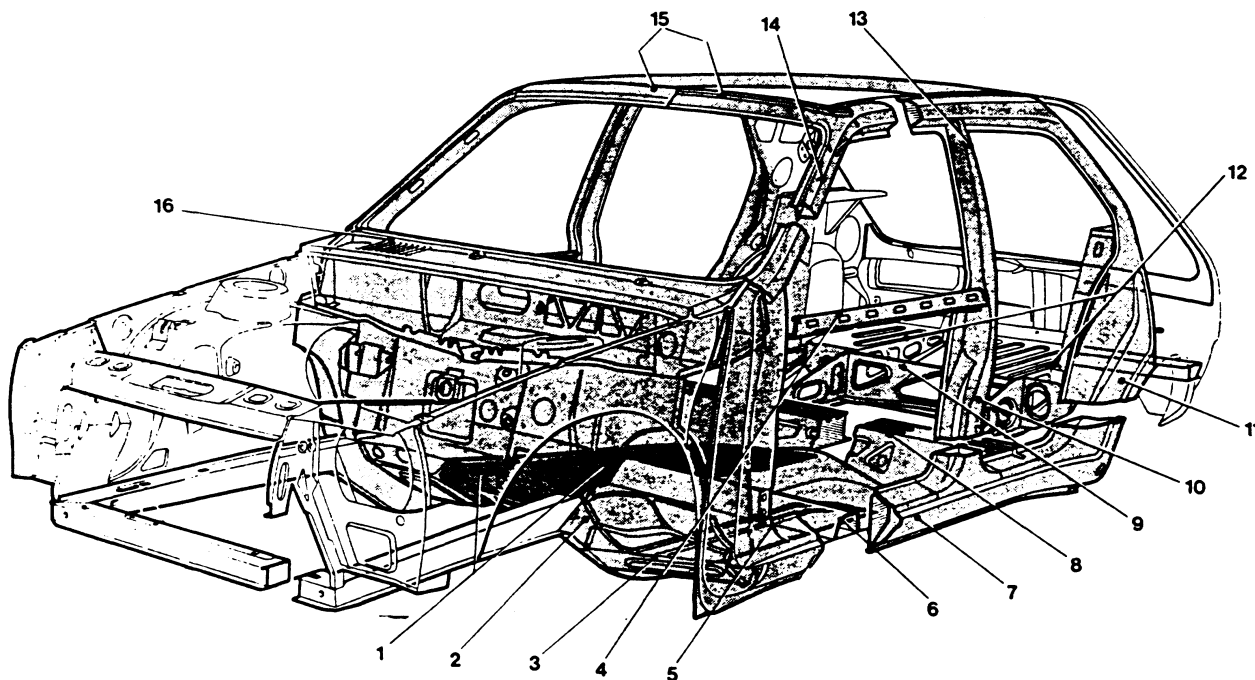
Conjunto estructural de protección del habitáculo de la carrocería de un RENAULT. 1, refuerzo del túnel en la plataforma. 2, extremo del travesaño delantero. 3, pieza de refuerzo. 4, refuerzo de la puerta delantera. 5, base del montante delantero. 6, travesaño para sustentación de los asientos delanteros. 7, estribo. 8, travesaño para sustentación del asiento trasero. 9, travesaño de sustentación de la suspensión trasera. 10, montante central. 11, montante trasero. 12, varas traseras. 13, parte alta del montante central. 14, montante delantero. 15, traviesa delantera del techo. 16, traviesa de la parte superior del salpicadero.
